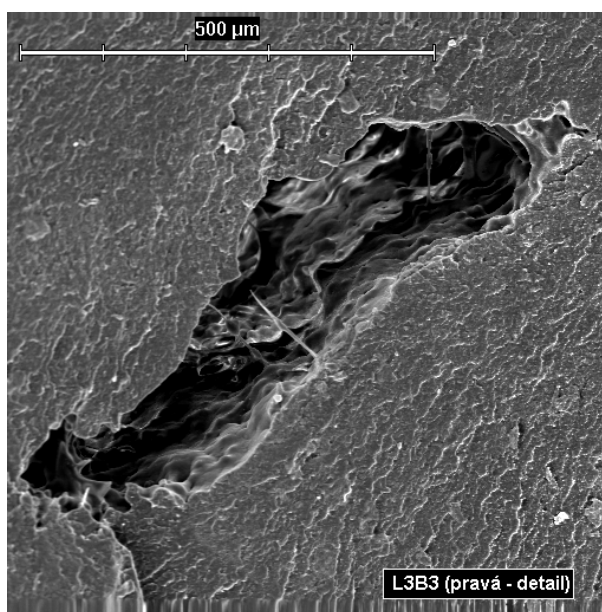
Detail místa lomu vzorku L3 – pravá strana a způsob plnění zkoumaného místa
